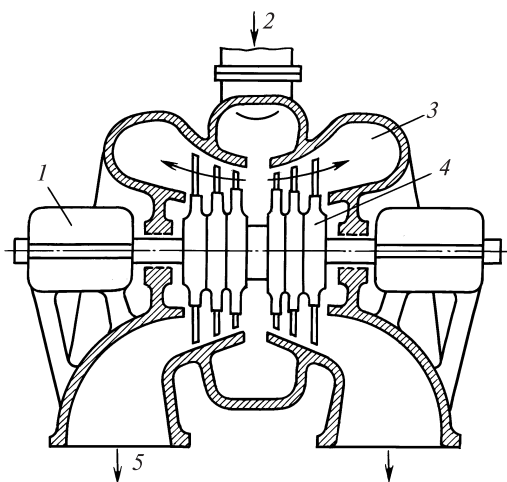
Конструктивная схема двухпоточного ЦНД
